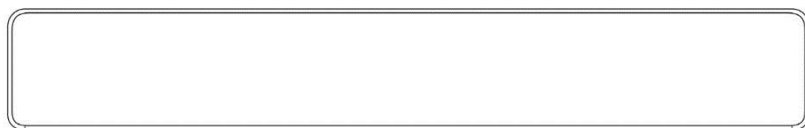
Profil plein de la planche « DecKorators » (également connue sous le nom de DecKorators Classic-Solid, DecKorators Vista-Solid ou DecKorators Heritage-Solid)
